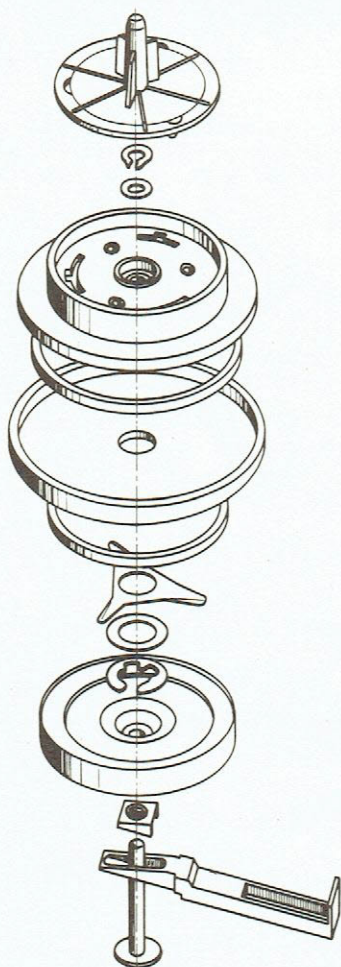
Vue éclatée de l'assiette bobineuse de gauche
